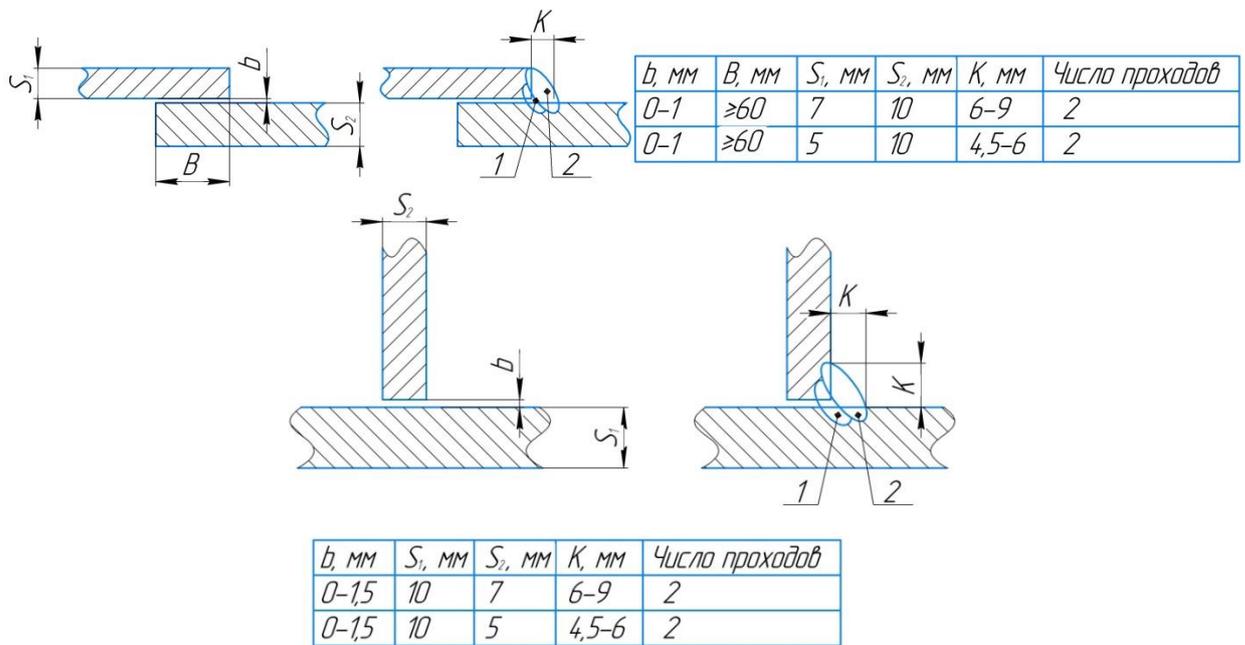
Геометрические размеры разделки кромок и размеры сварного шва по ГОСТ 14771-76
